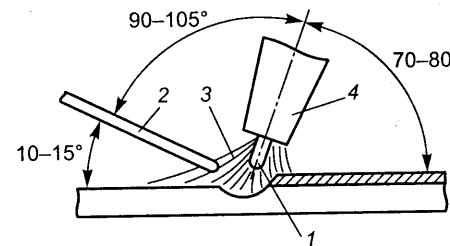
Расположение горелки и присадочного прутка при ручной аргонодуговой сварке:
